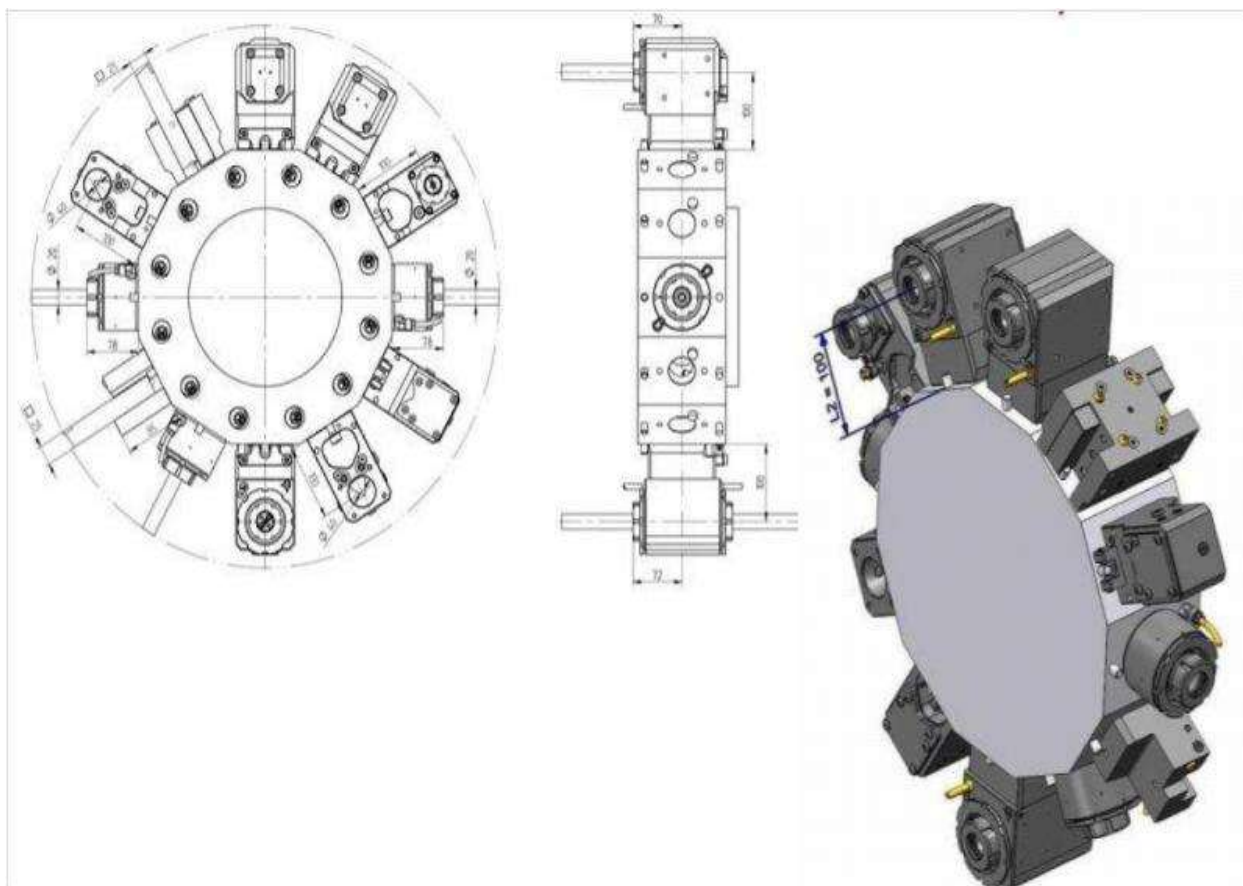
Револьверна головка VDI з державками для токарного і приводного інструмента[3]
